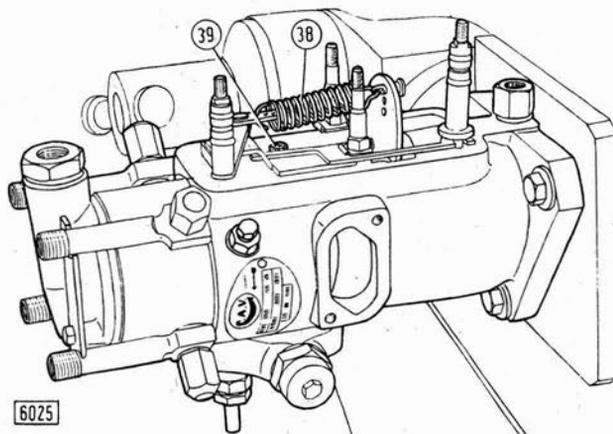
Vue du régulateur de vitesse le couvercle étant déposé.
